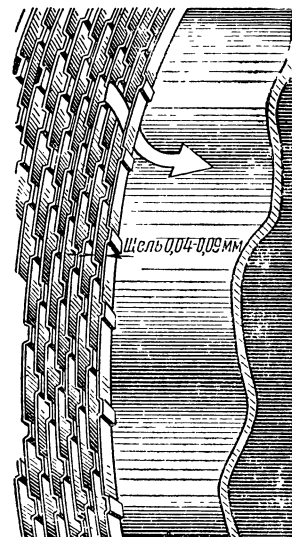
Вид фильтрующей ленты и гофрированного цилиндра фильтра грубой очистки топлива.
